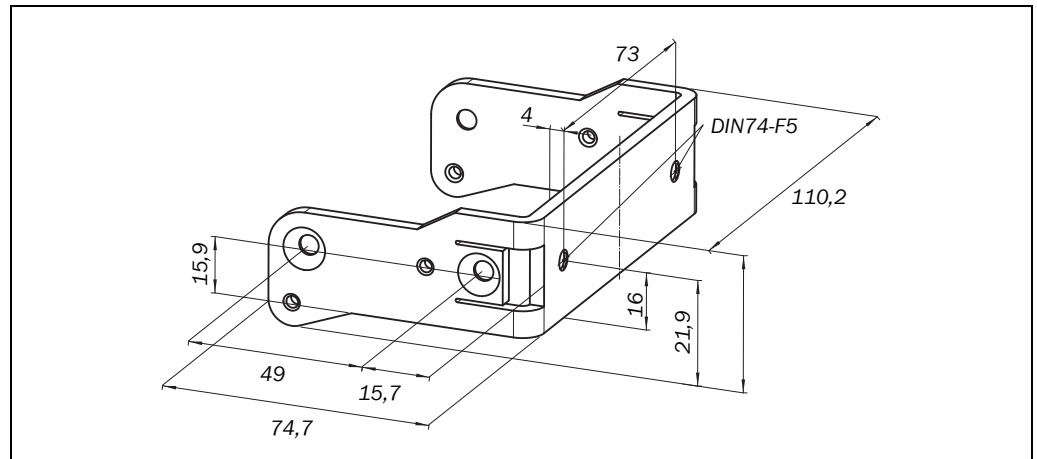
Maßbild Befestigungssatz 1b (mm)
